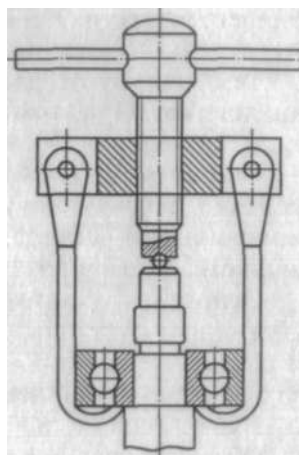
Схема снятия внутреннего кольца подшипника, напрессованного на вал
